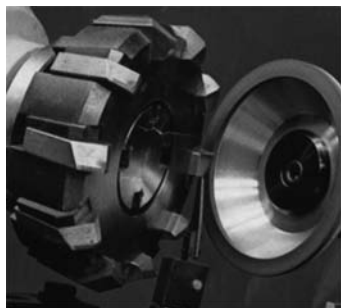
Заточка ножа фрезерной головки по вспомогательной задней поверхности
